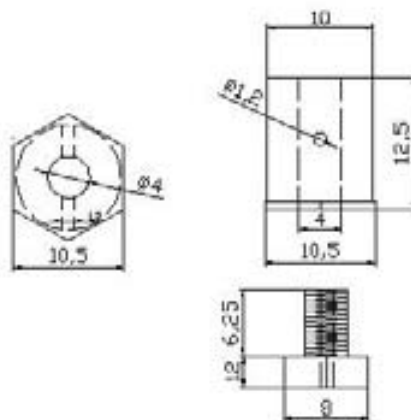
Detalhamento esquemático do parafuso trava de fios de SMA no suporte de fixação, dimensões em mm.
